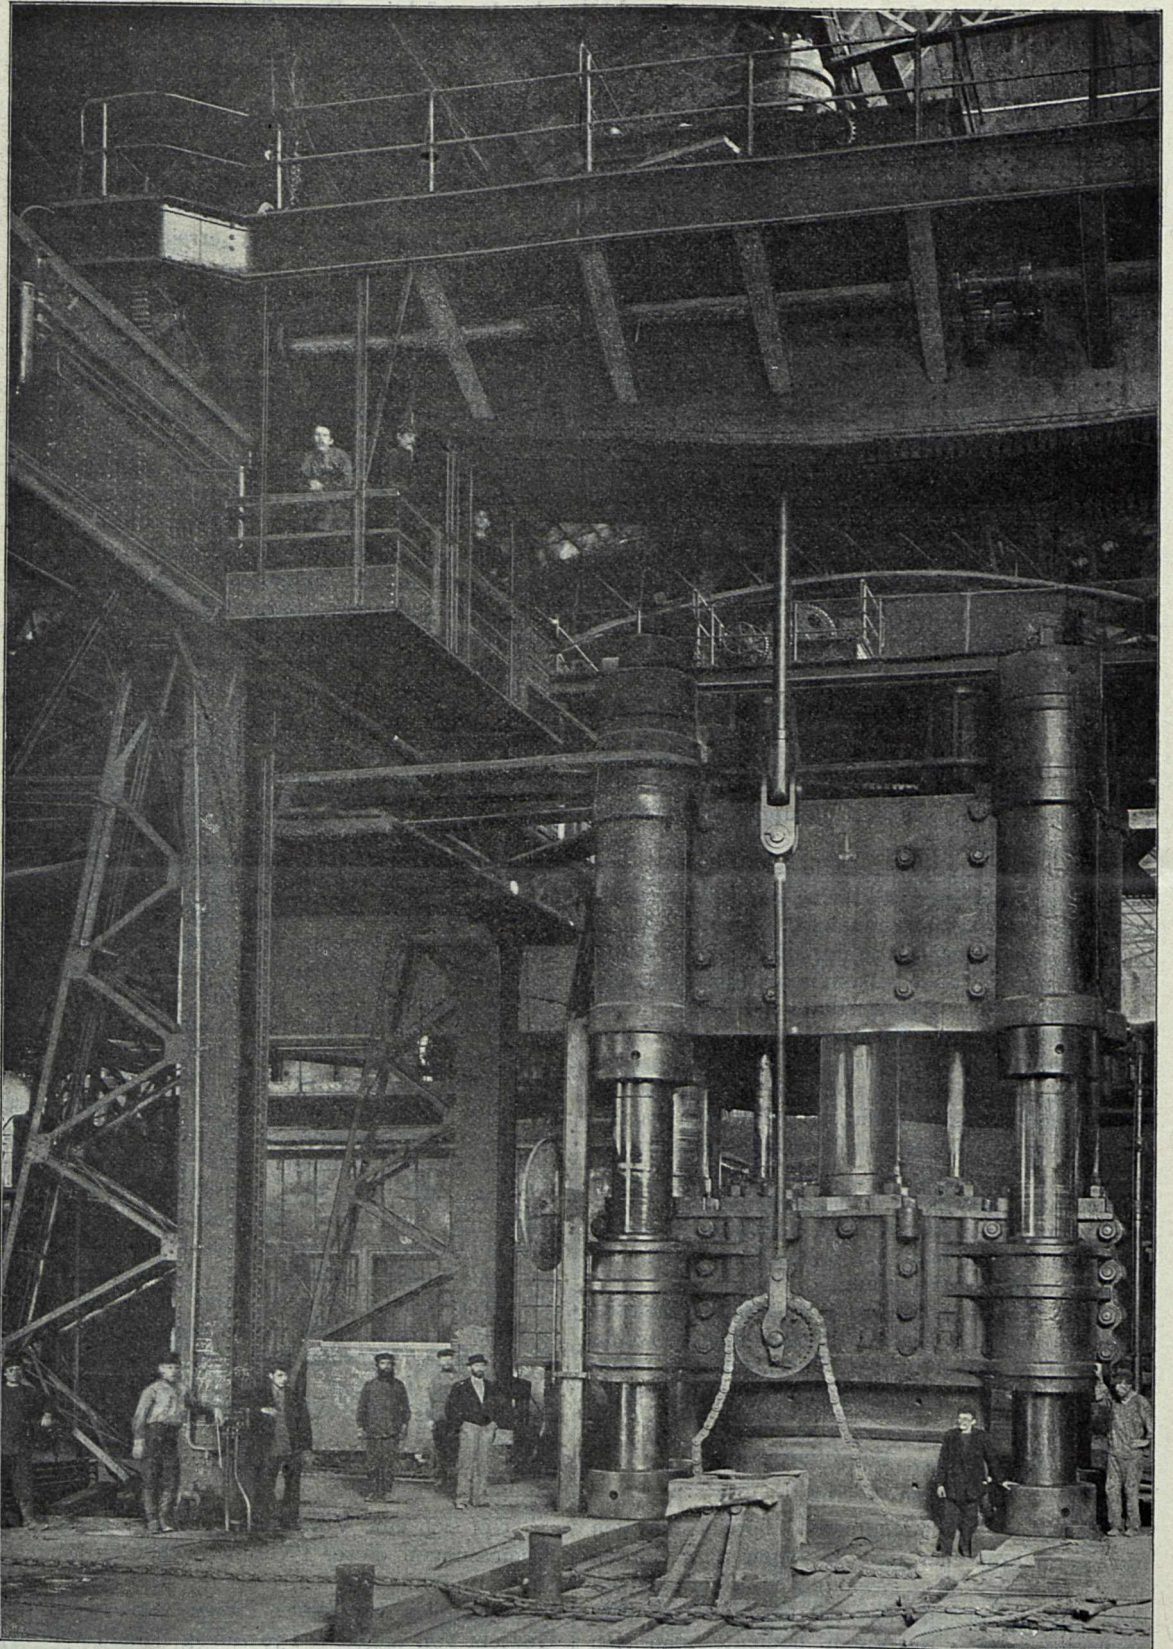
Hydraulische Schmiedepresse für 1000000 kg Druck,
